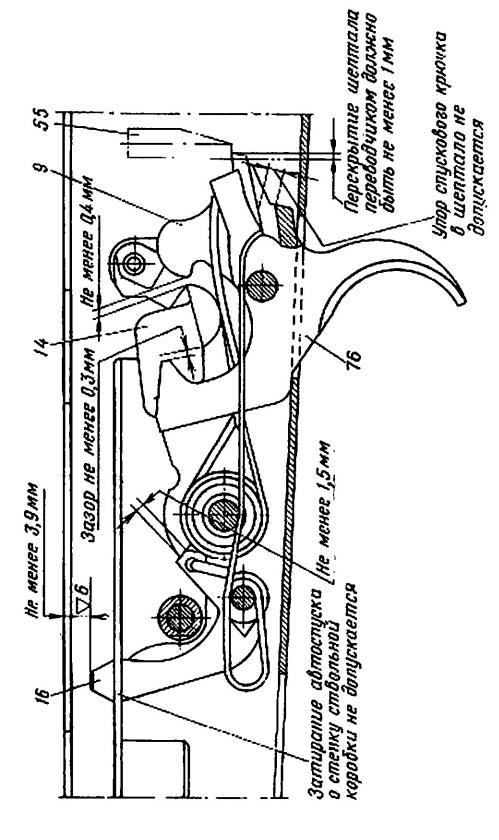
Зачистка шептала автоспуска и обработка после наплавки конца рычага автоспуска
